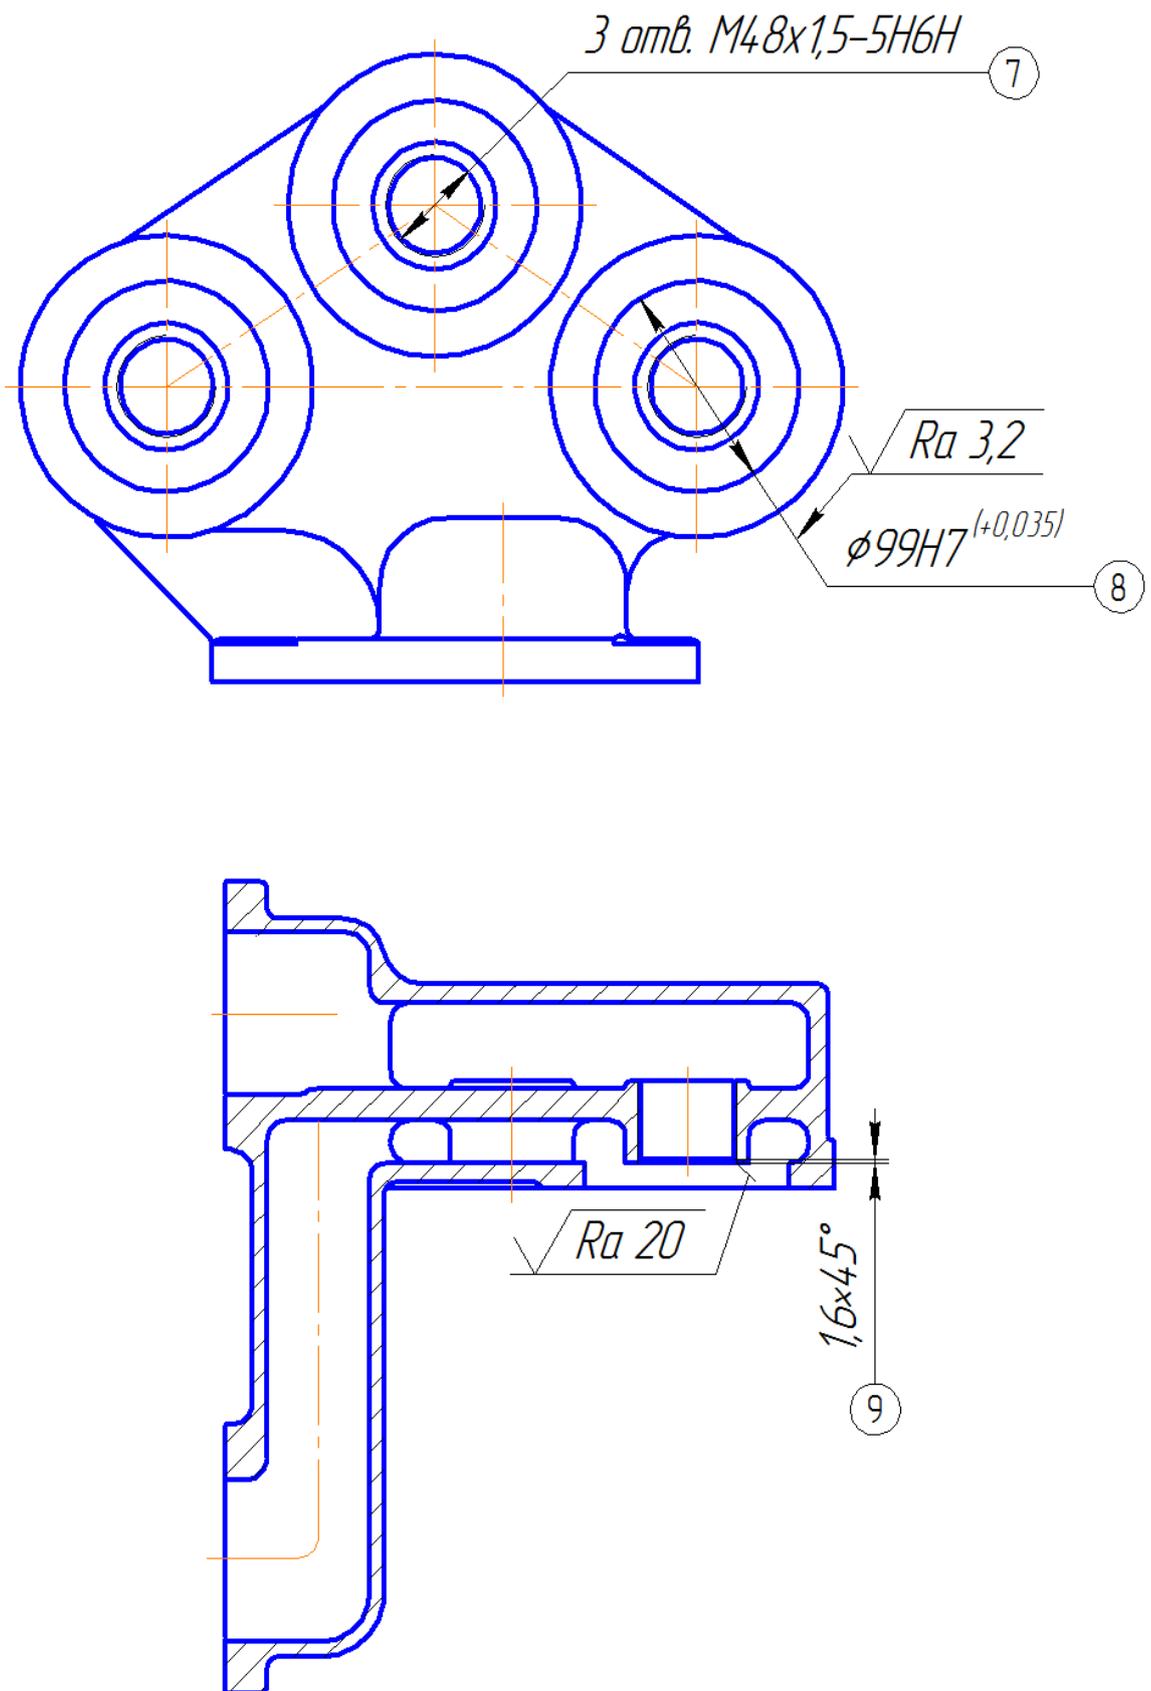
Эскиз детали «Корпус масляного фильтра»
